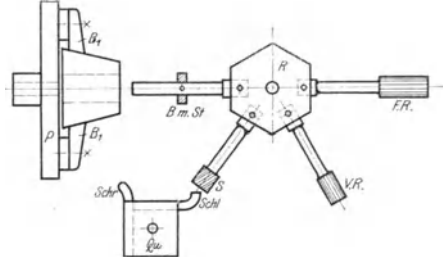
Herstellen der Bohrung und Bearbeiten einer Stirnfläche.
